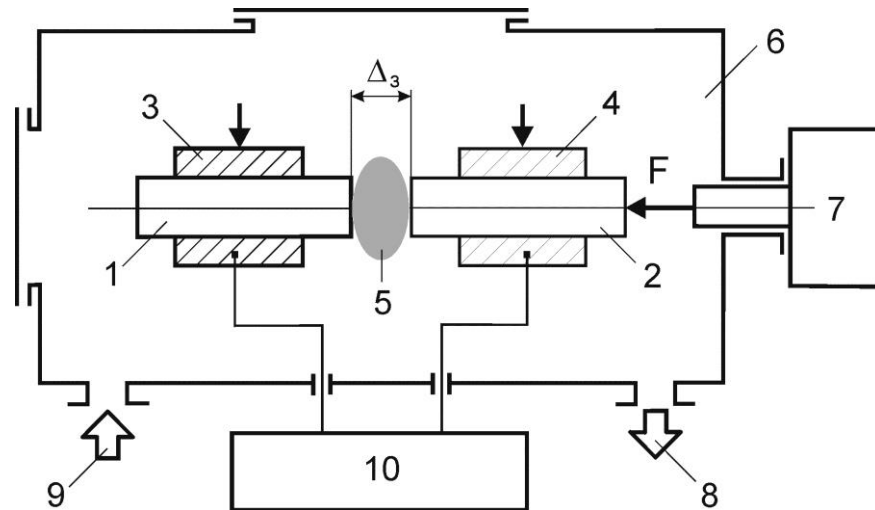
Схема стыковой сварки дугой низкого давления:
